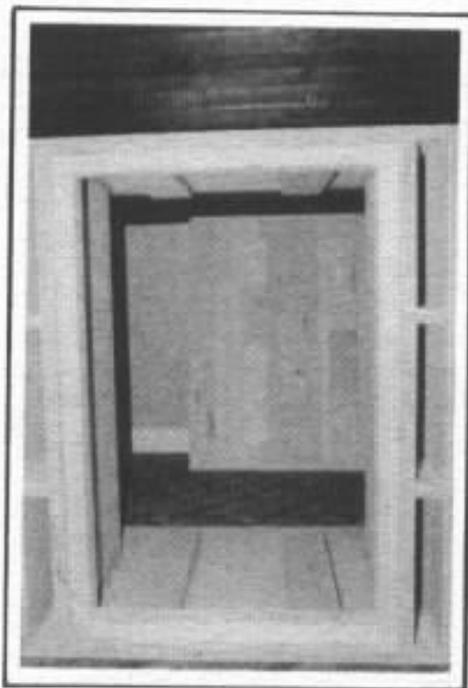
Assemblage proprement dit. Noter l'emplacement des serre-joints pour le vissage des éléments externes des filtres. Le serre-joint transversal sera déplacé pour visser les éléments internes de façon à assurer un ajustage parfait.
